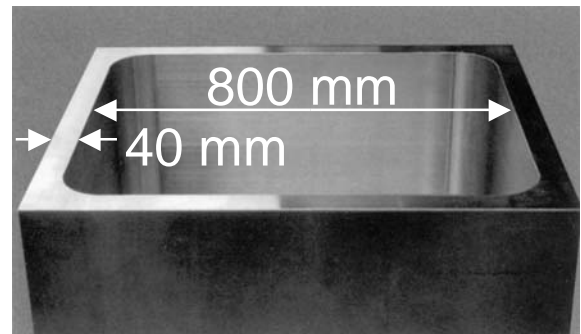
Aluminium-Kammer Elektronenstrahlgeschweißte, gefräst
